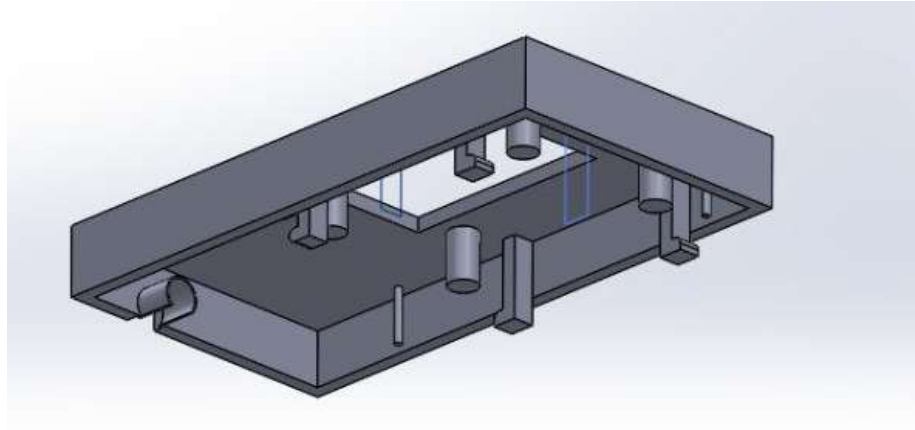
3D конструкція верхньої частини корпусу
